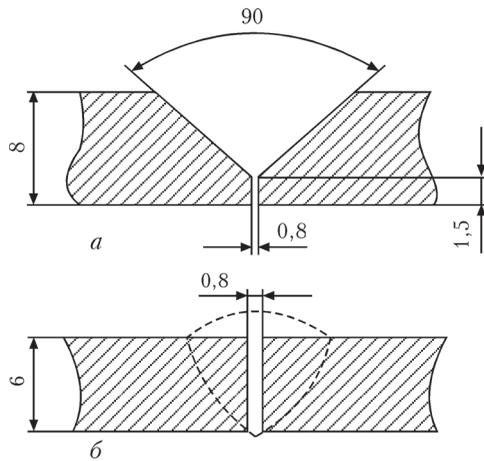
Схема разделки кромок для АДС: *а* — односторонняя сварка с разделкой кромок и подачей присадочной проволоки марки СП15св; *б* — односторонняя сварка без разделки кромок с подачей присадочной проволоки марки ВТ1-00св
